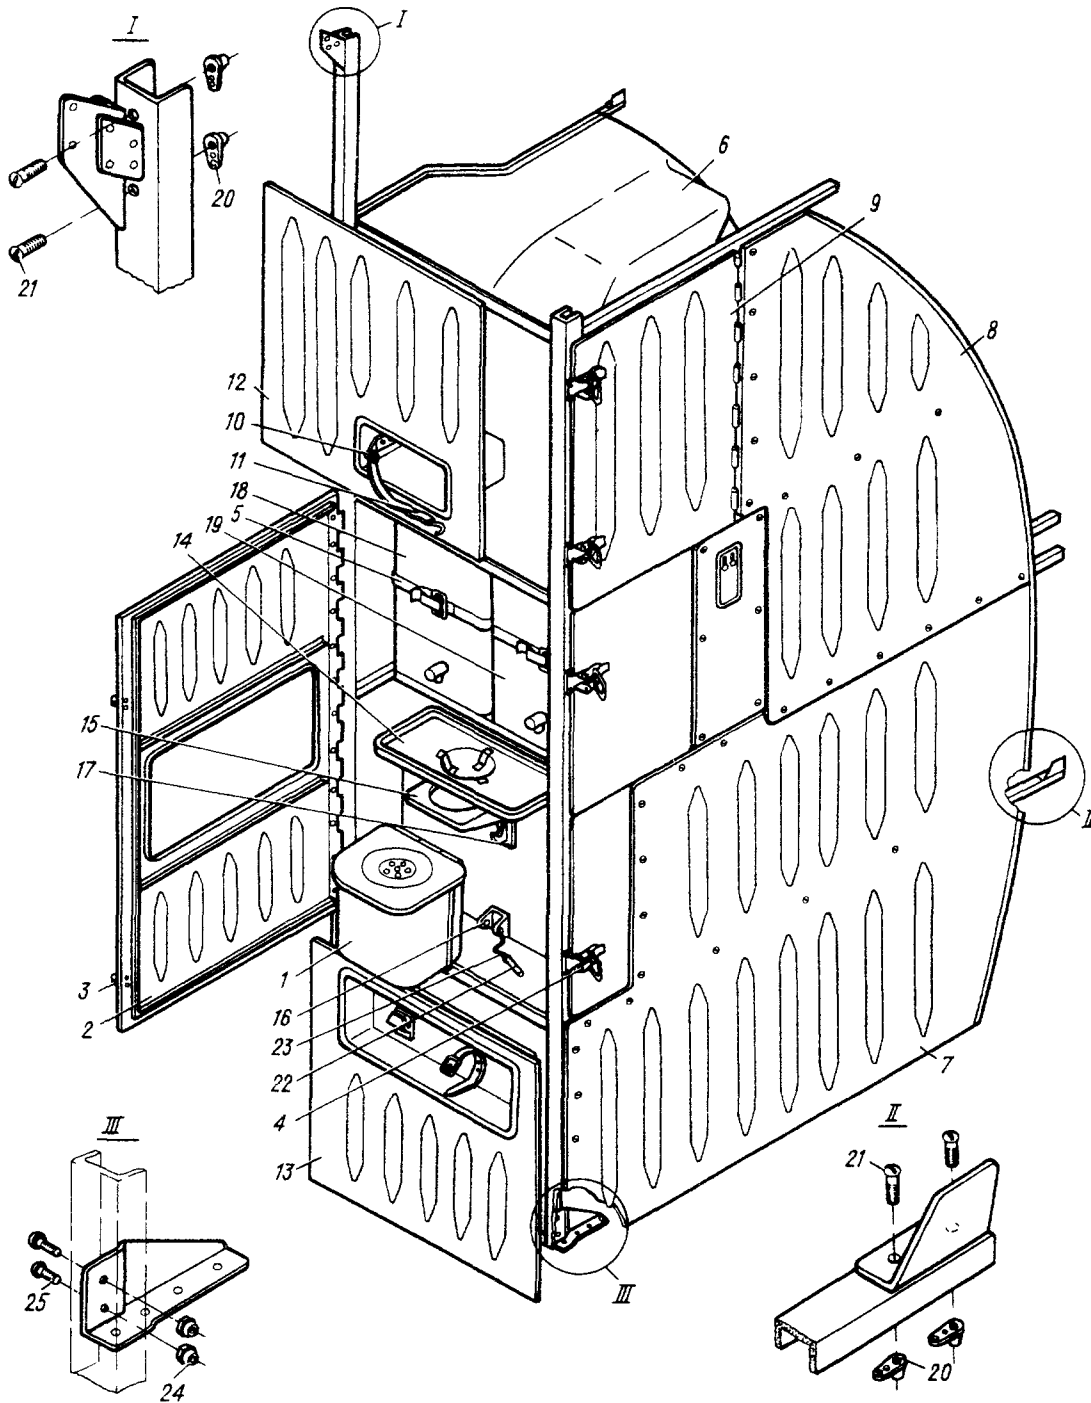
УСТАНОВКА ЭТАЖЕРКИ СО СПЕЦБОРУДОВАНИЕМ
